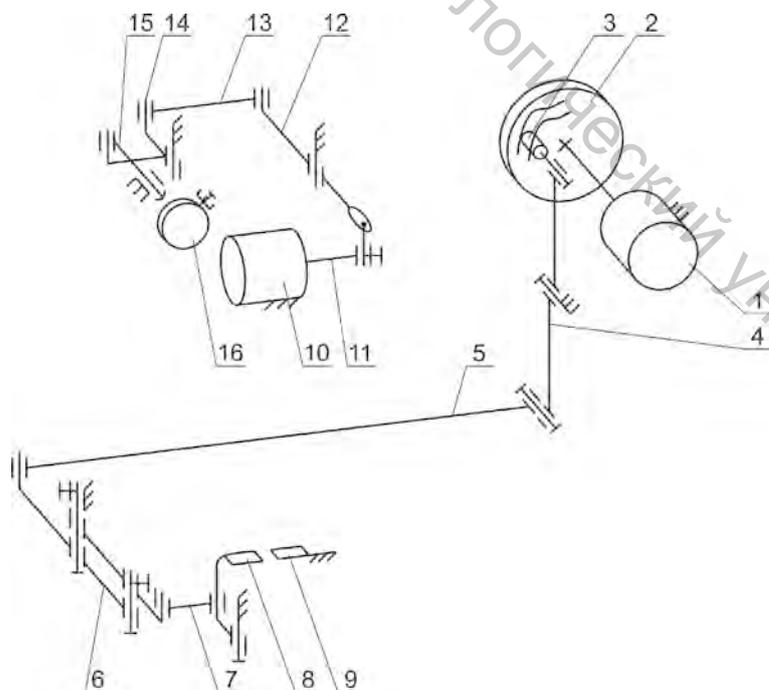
Кинематическая схема механизмов обрезки ниток и освобождения натяжения игольной нитки
